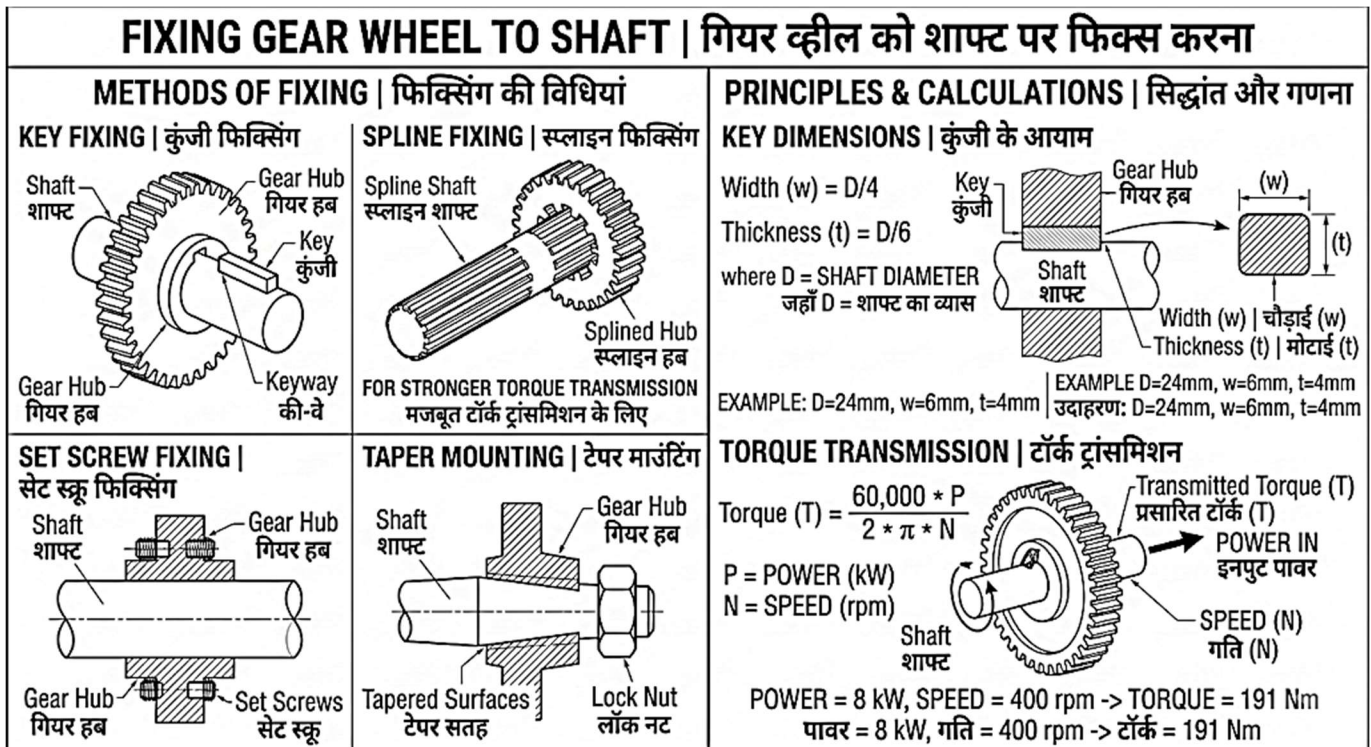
Methods of Fixing Gear Wheels to Shafts | गियर व्हील को शाफ्ट पर फिक्स करने की विधियाँ
